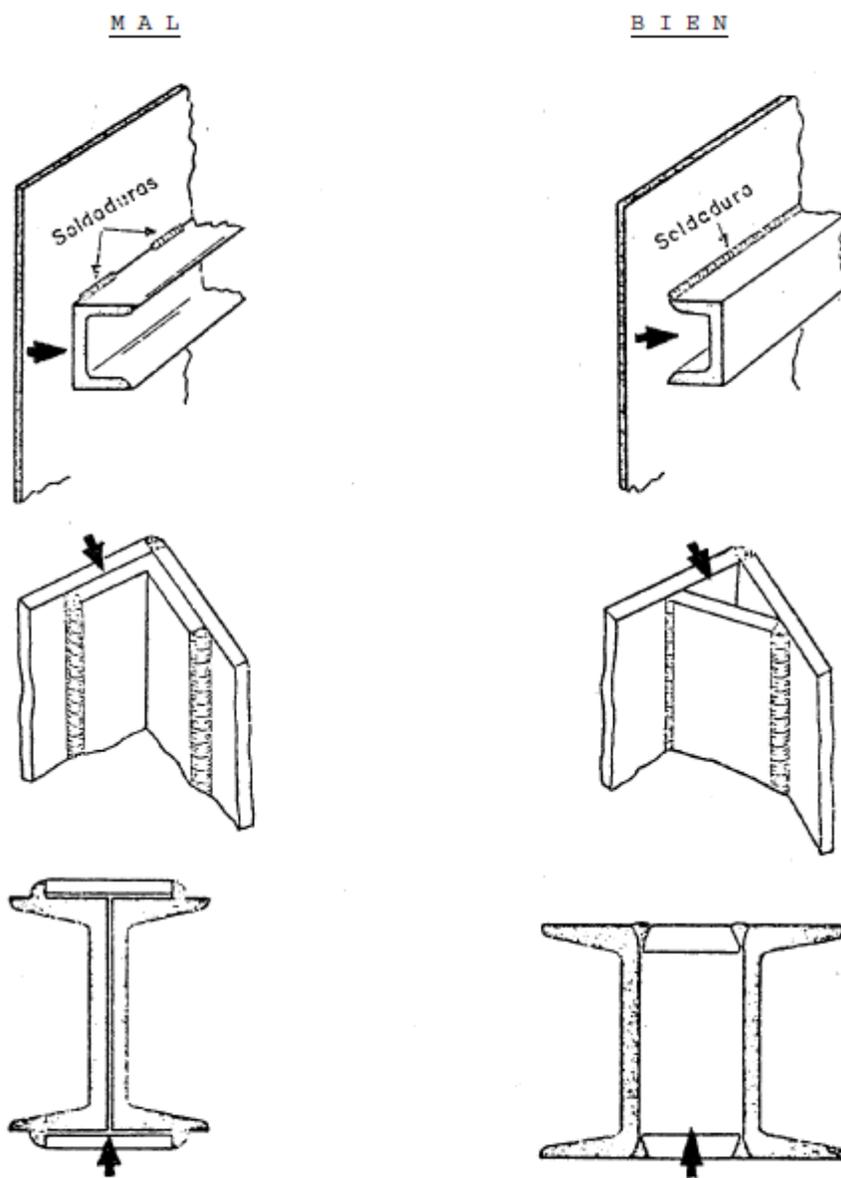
Sellado total, por soldadura, de las superficies en contacto
